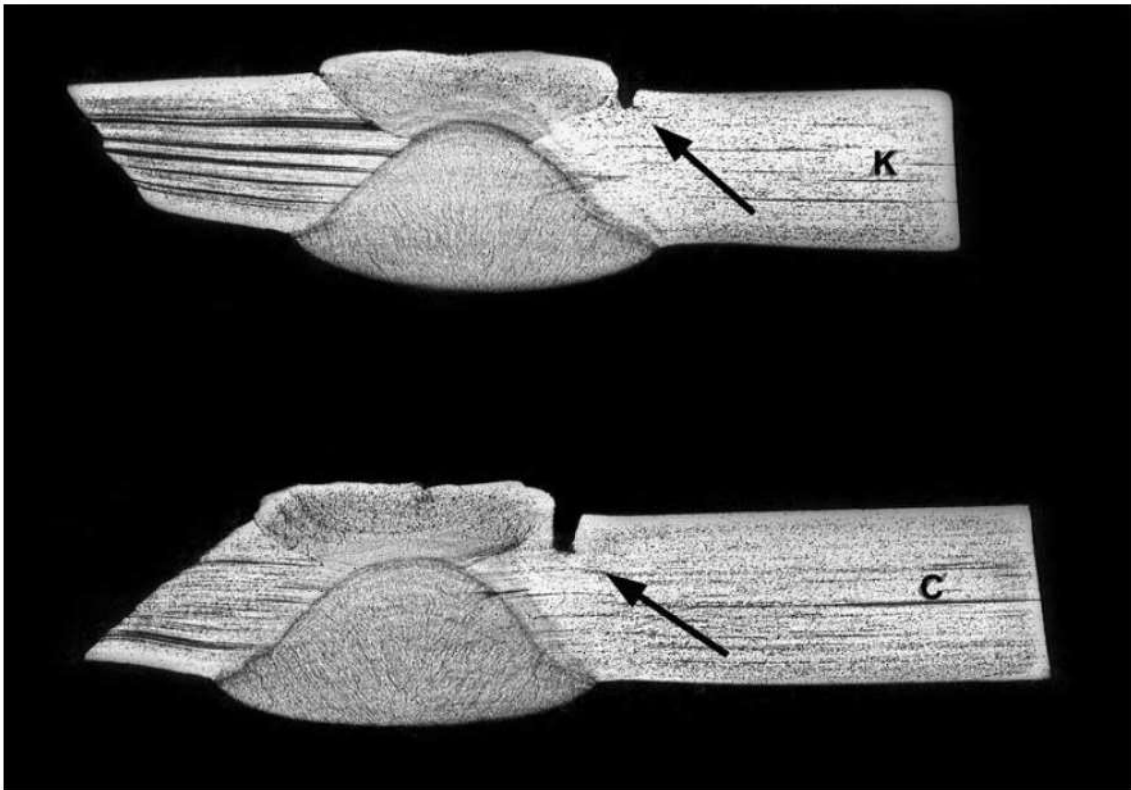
Sección transversal de la superficie de fractura y de la soldadura en los tramos K (pieza superior) y C (pieza inferior) señalados en la figura 3. Ataque con reactivo de yodo. Las grietas (flechas) que se notan junto a la soldadura son reproducidos con mayor detalle en la figura 5. Reactivo de yodo. 1.5X.
